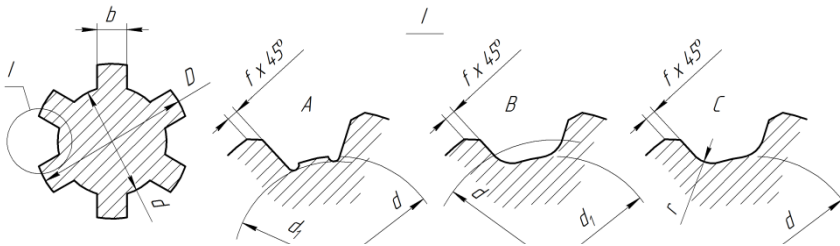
Конструктивні параметри шліфувального вала
